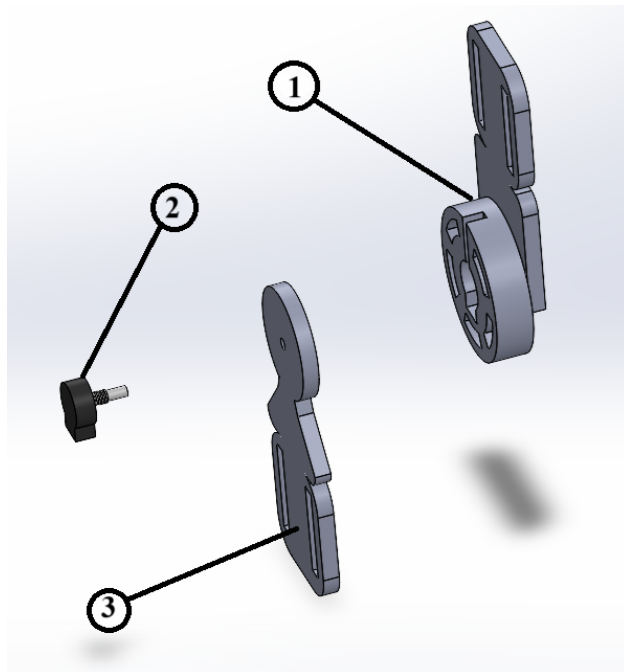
Partes de la estructura mecánica del dispositivo de rodilla.
